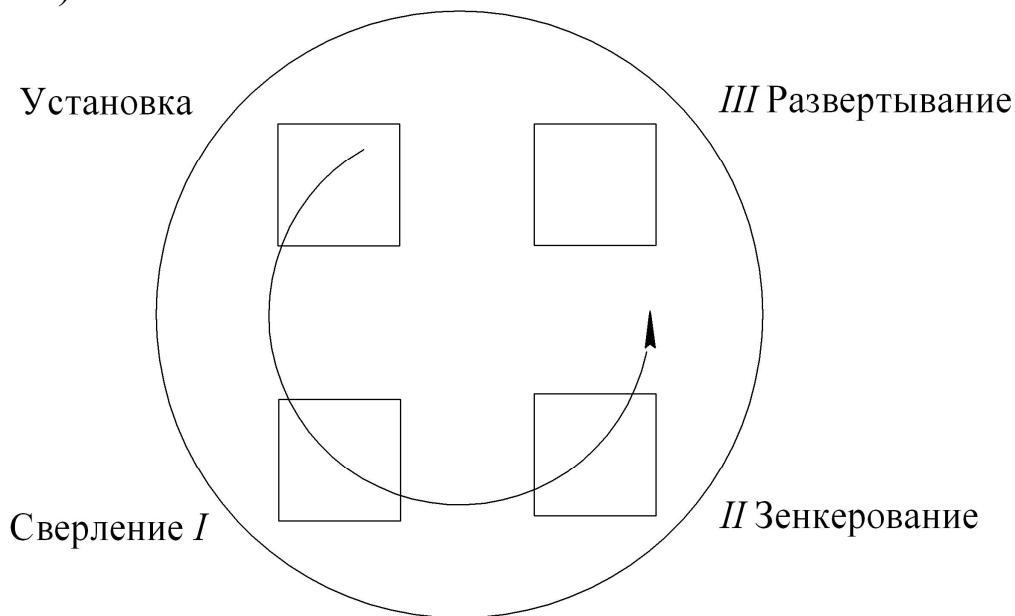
Обработка заготовки на четырехпозиционном станке
